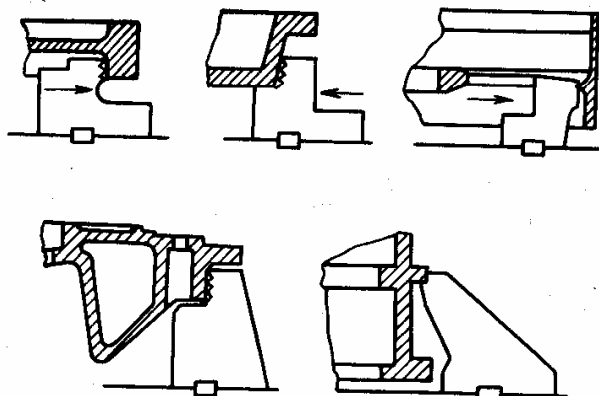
Схеми закріплення заготовок на планшайбі верстата
